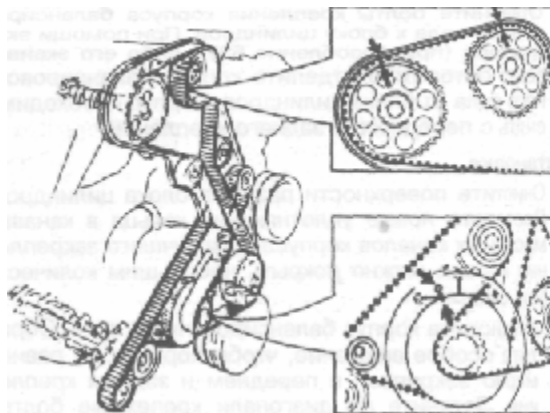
Снятие приводного ремня и ремня балансировочных валов — Двигатель В234F
